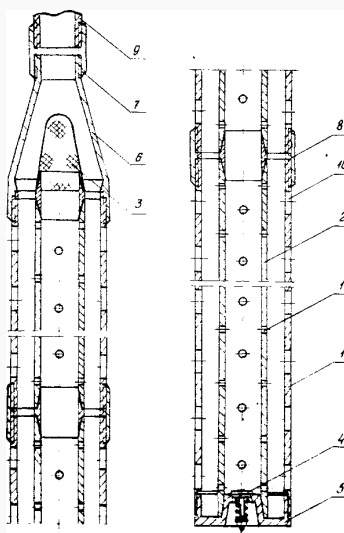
Пристрій для термохімічної обробки свердловин:
